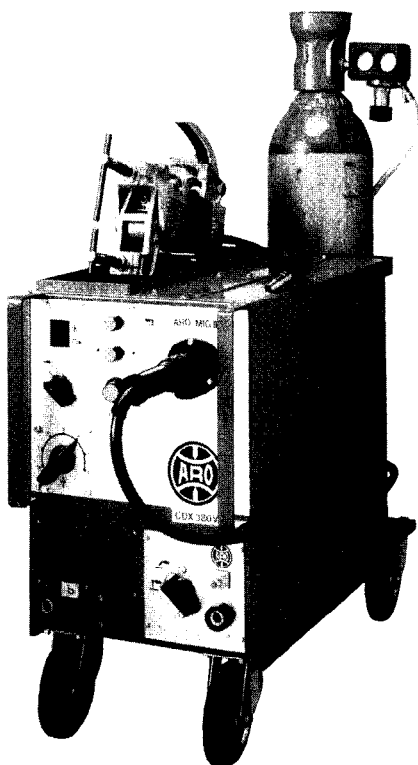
Conjunto de soldadura Aro Mig II, CDX 380 V, de alto rendimiento para un taller de planchistería.
